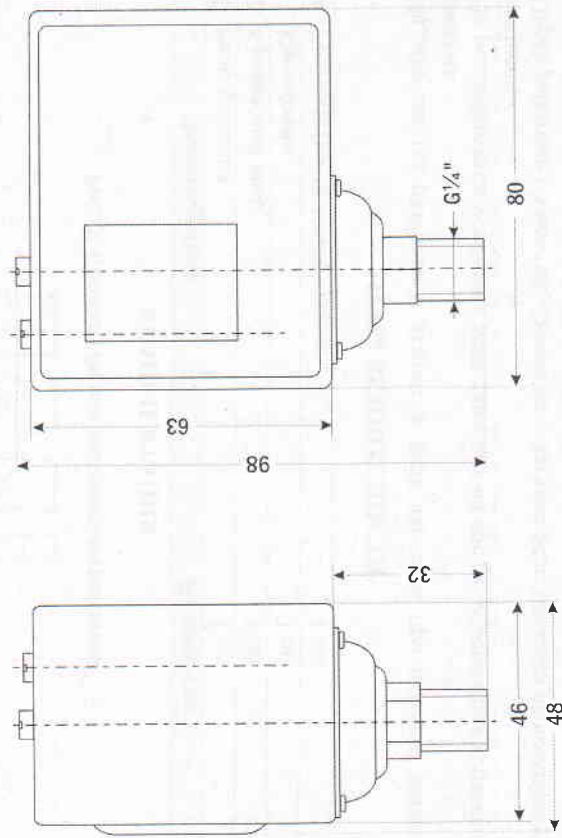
Габаритные и установочные размеры датчика-реле давления
